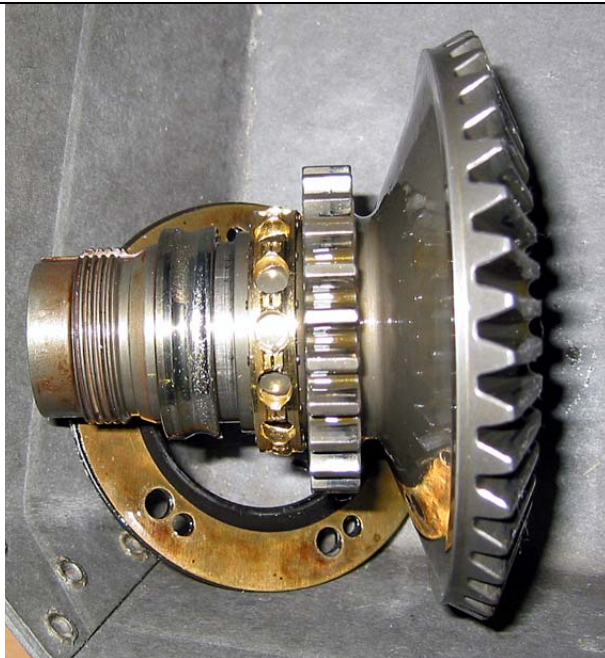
Kegelrad *accessory drive gear assembly* in ausgebautem Zustand mit schadhaftem Lager und Spurrillen auf dem Lagerinnenring
